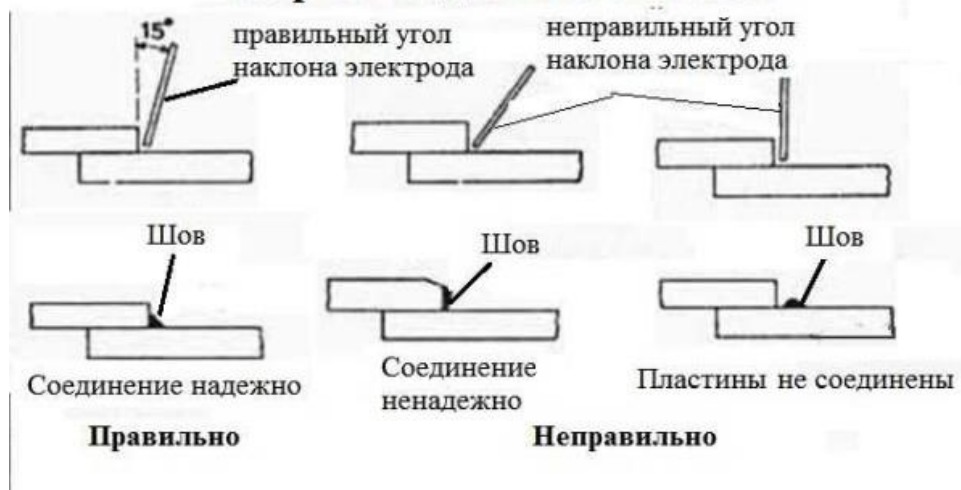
Как правильно держать электрод при сварке внахлест
